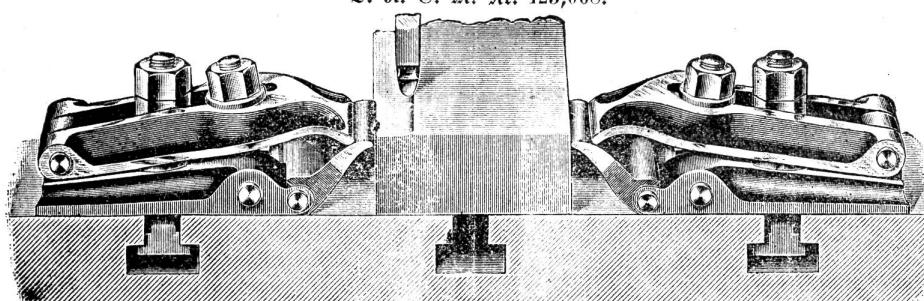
Im Gebrauch auf der Hobelmaschine.
